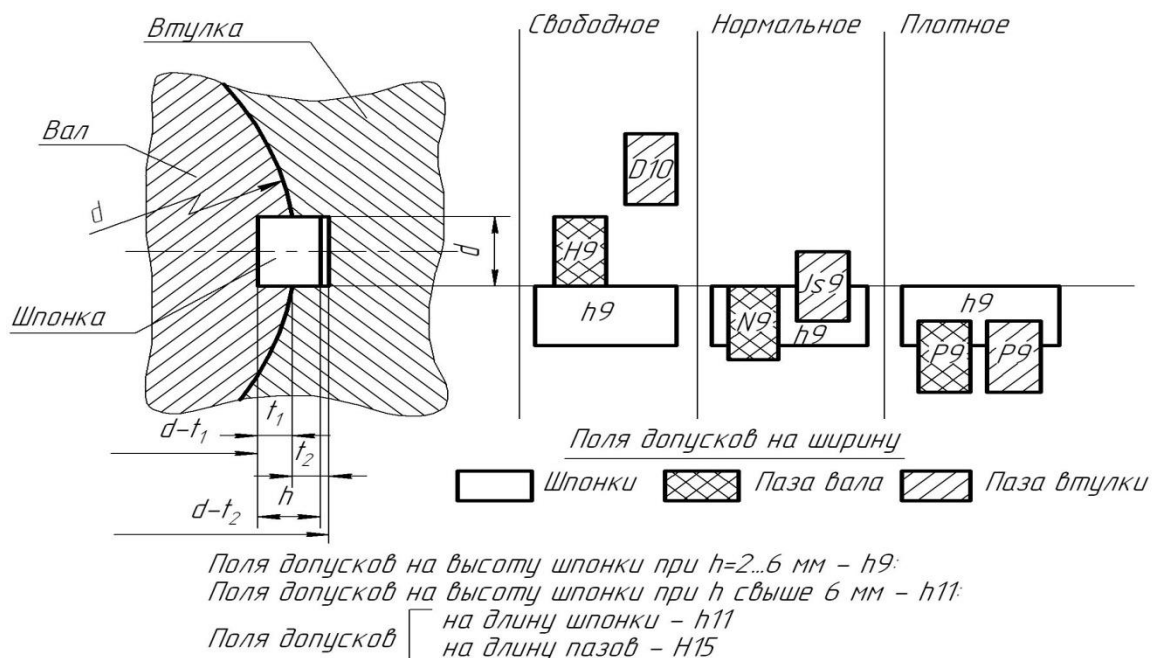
Рекомендуемые посадки и поля допусков для соединения с призматическими шпонками
